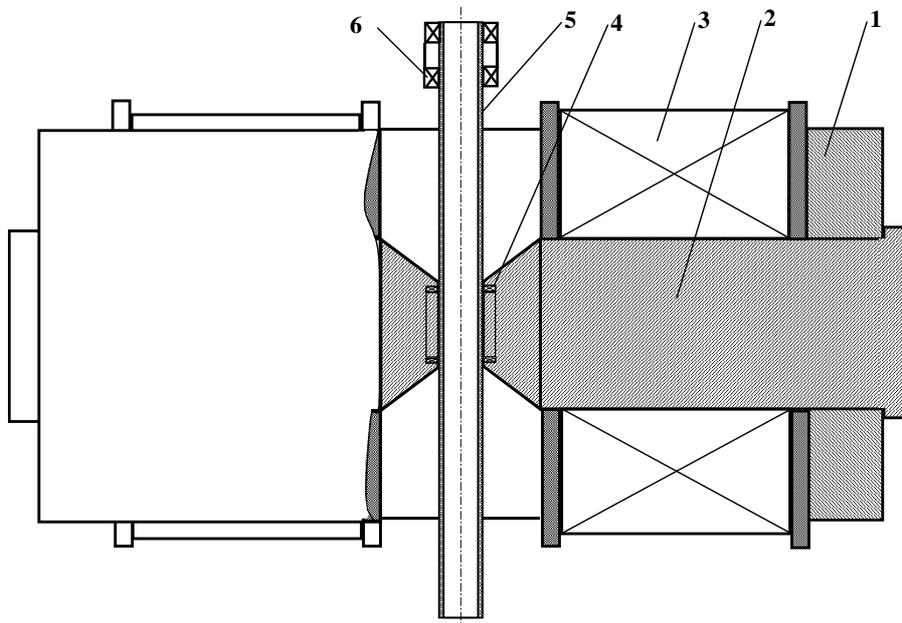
Конструкция НСПТ для ПМ, намагниченных поперек продольной оси
